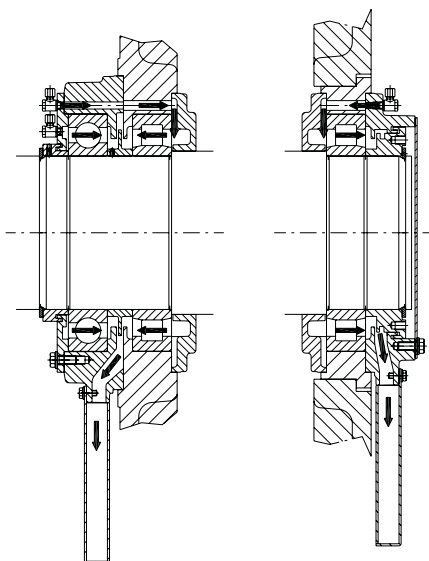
Пример смазочного канала, проходящего через подшипниковый узел горизонтальной машины
